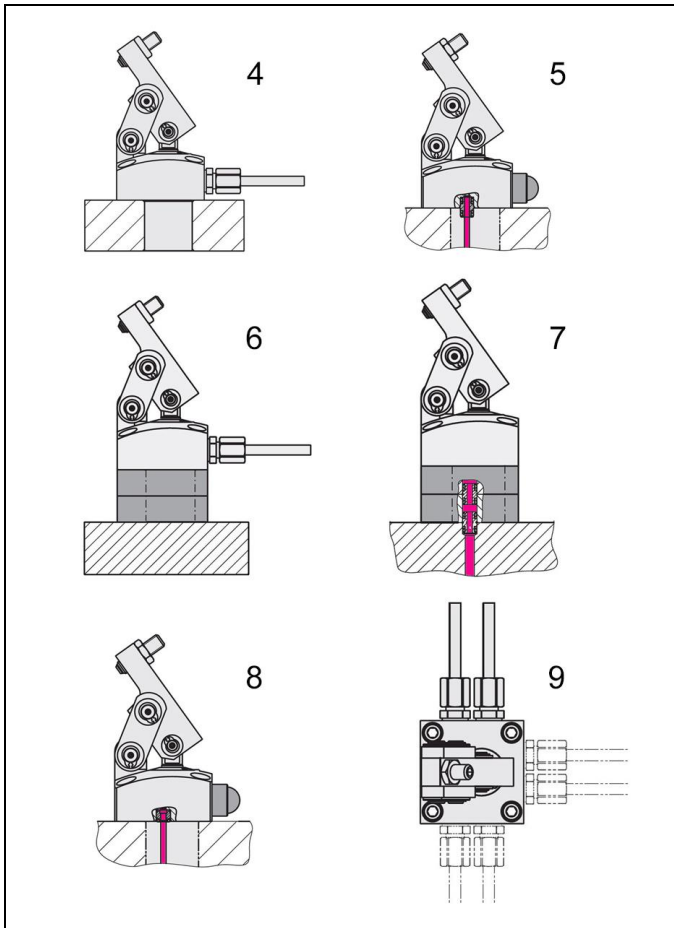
Befestigungsmöglichkeiten Anschluss Rohrgewinde und Steckverbinder
